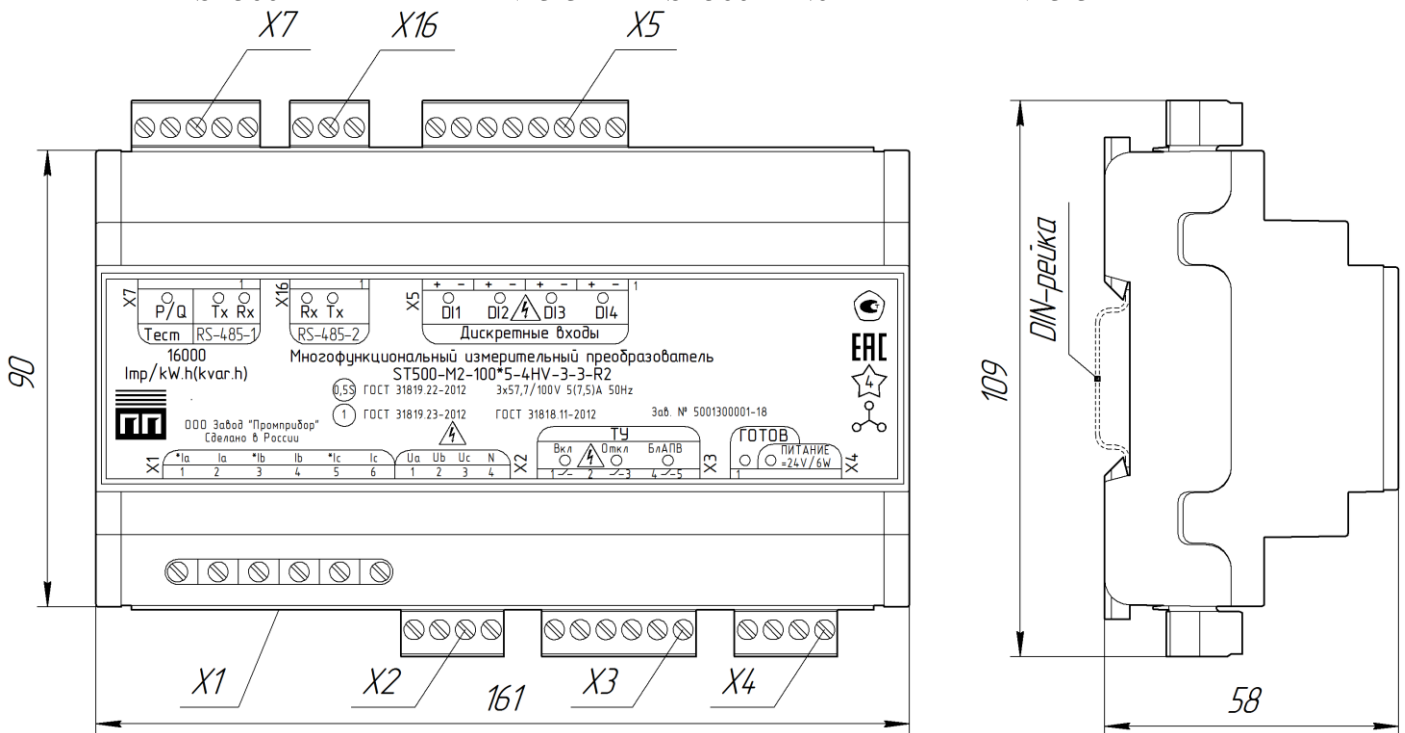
Внешний вид и габаритные размеры МИП ST500-M2-XXX*X-4HV-3-3-R2 и ST500-M2.02-XXX*X-4HV-3-3-R2
